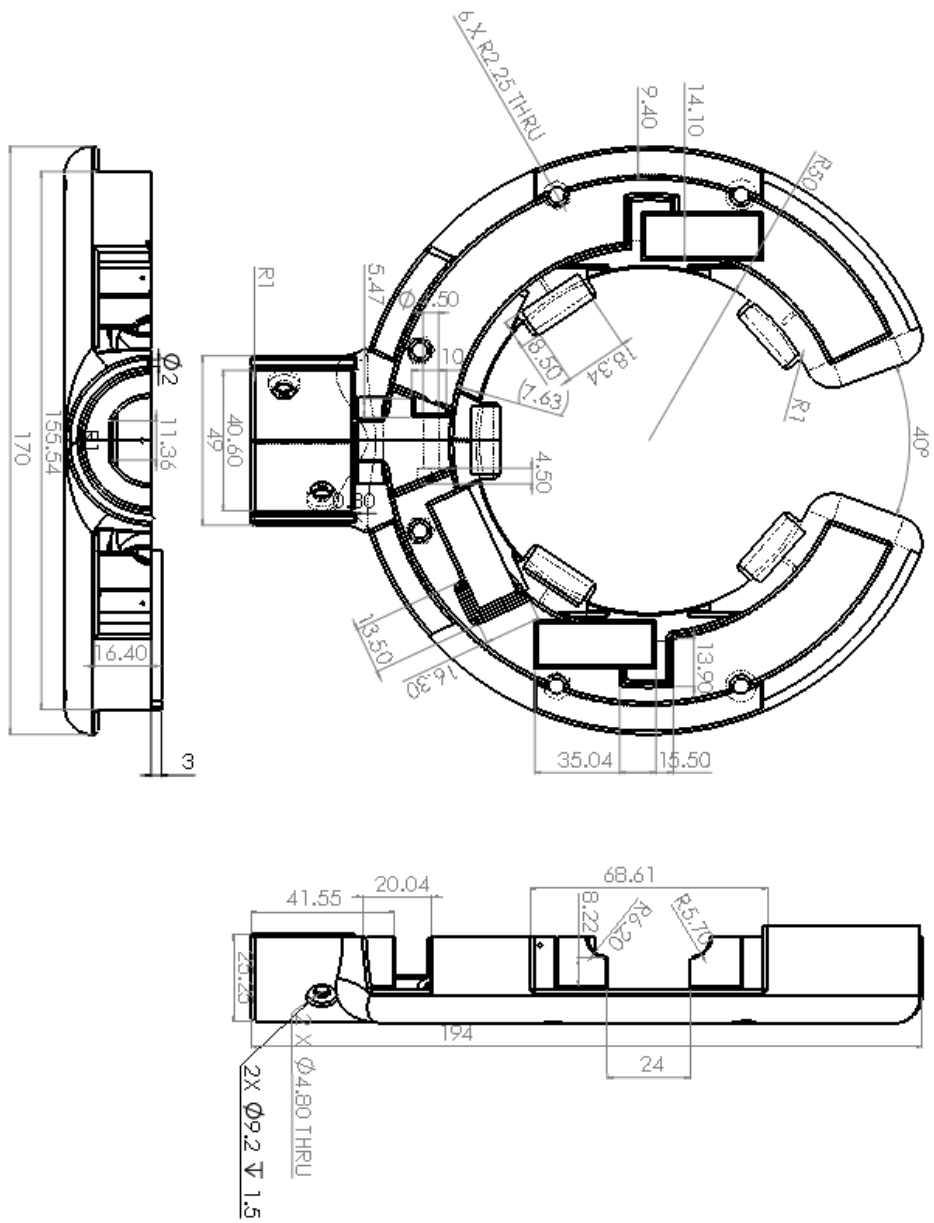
Estrutura principal do dispositivo, lado 1. O lado 2 é simétrico segundo o plano apresentado na vista central do desenho e segundo o plano transversal a este.
